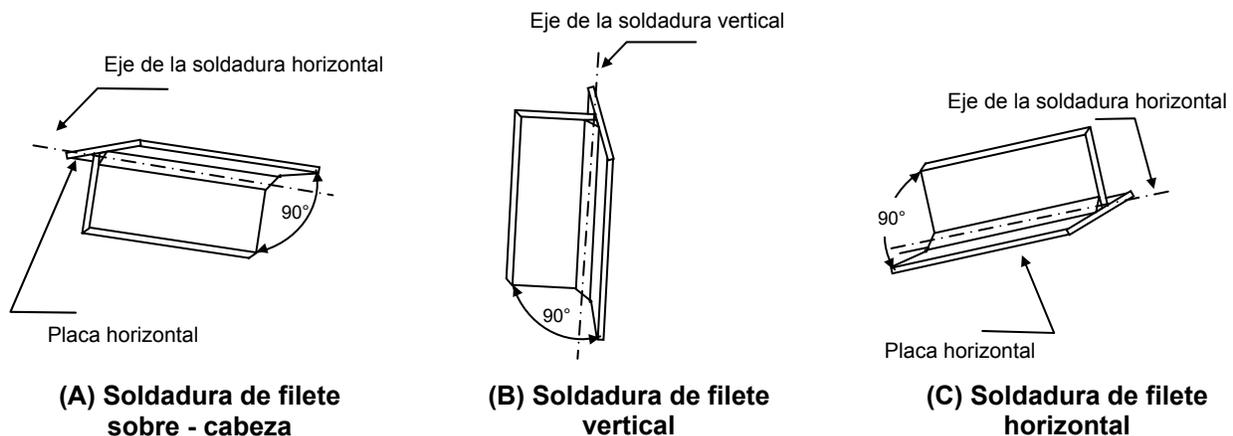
POSICIONES DE SOLDADURA PARA LAS PROBETAS DE SOLDADURA DE FILETE.
